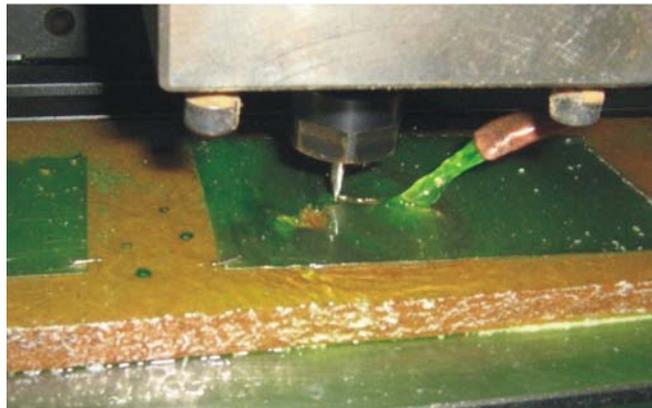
Processo de usinagem CNC de chapas de titânio para a fabricação das peças de joalheria.
